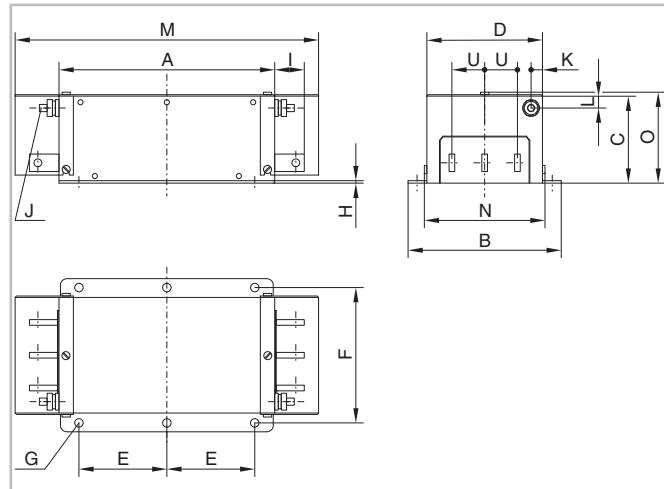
Габаритный чертеж RFI фильтров 3259-320-99 .. 3259-600-99
